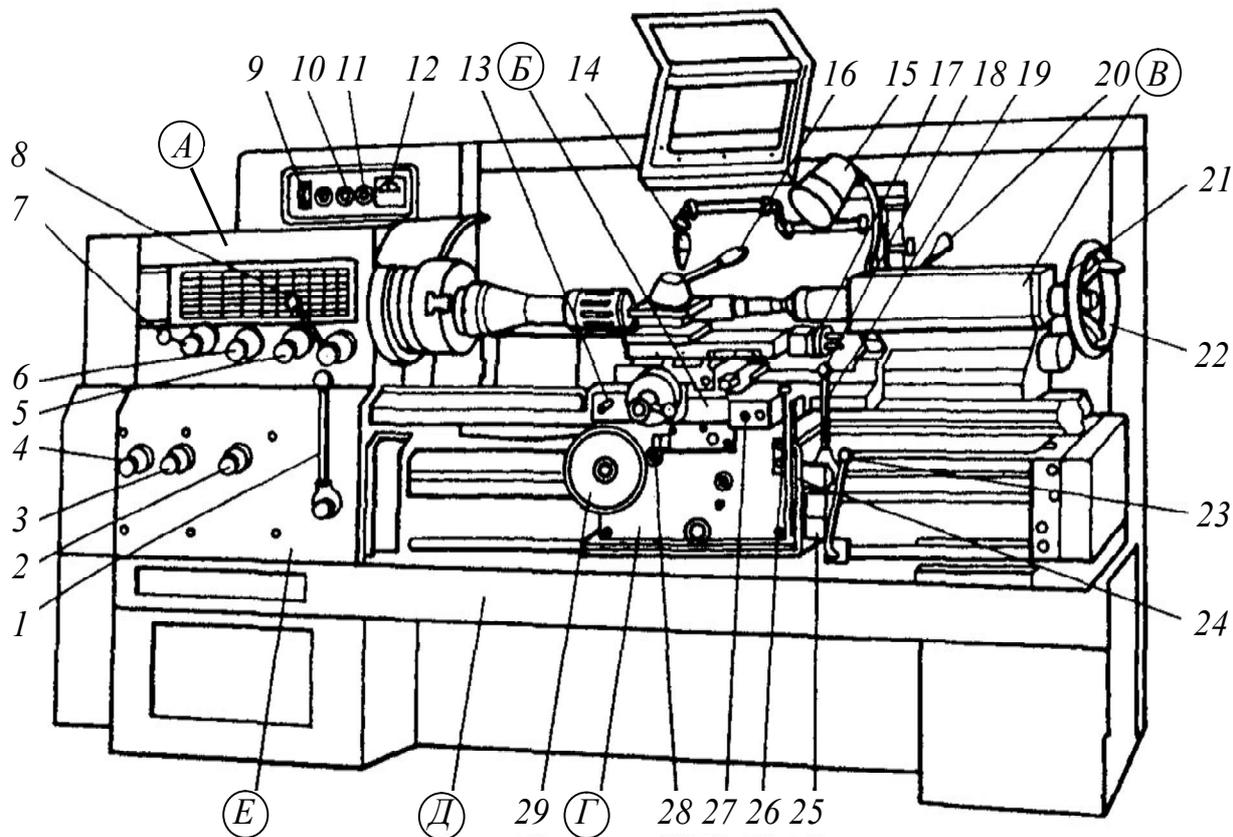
Токарно-винторезный станок 16К20 и органы его управления
